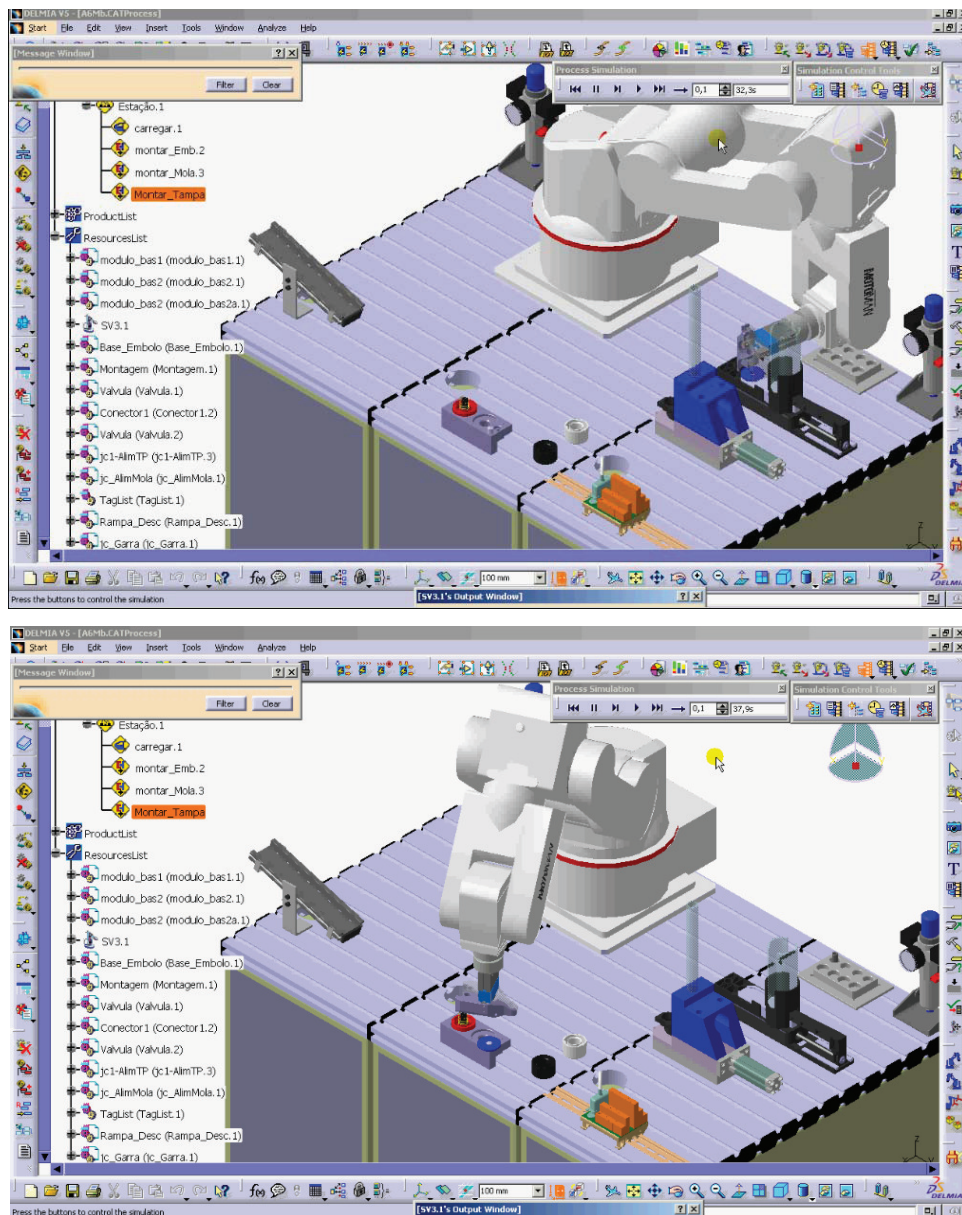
Coleta da tampa em seu magazine e teste da posição da tampa para montagem
